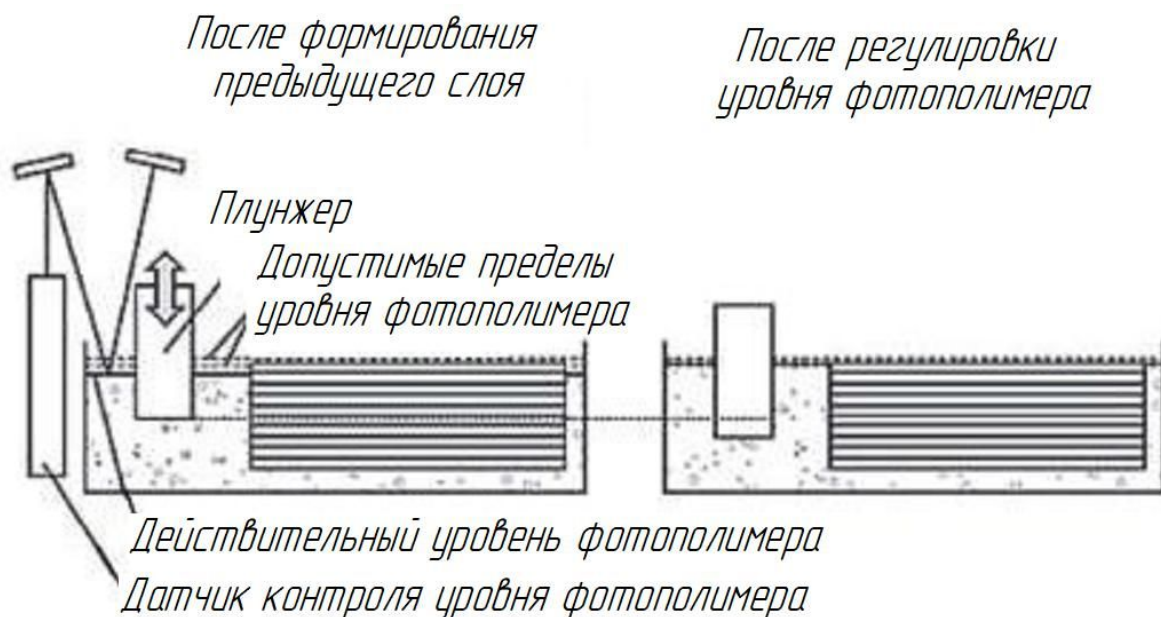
Схема контроля и регулировки уровня фотополимера
